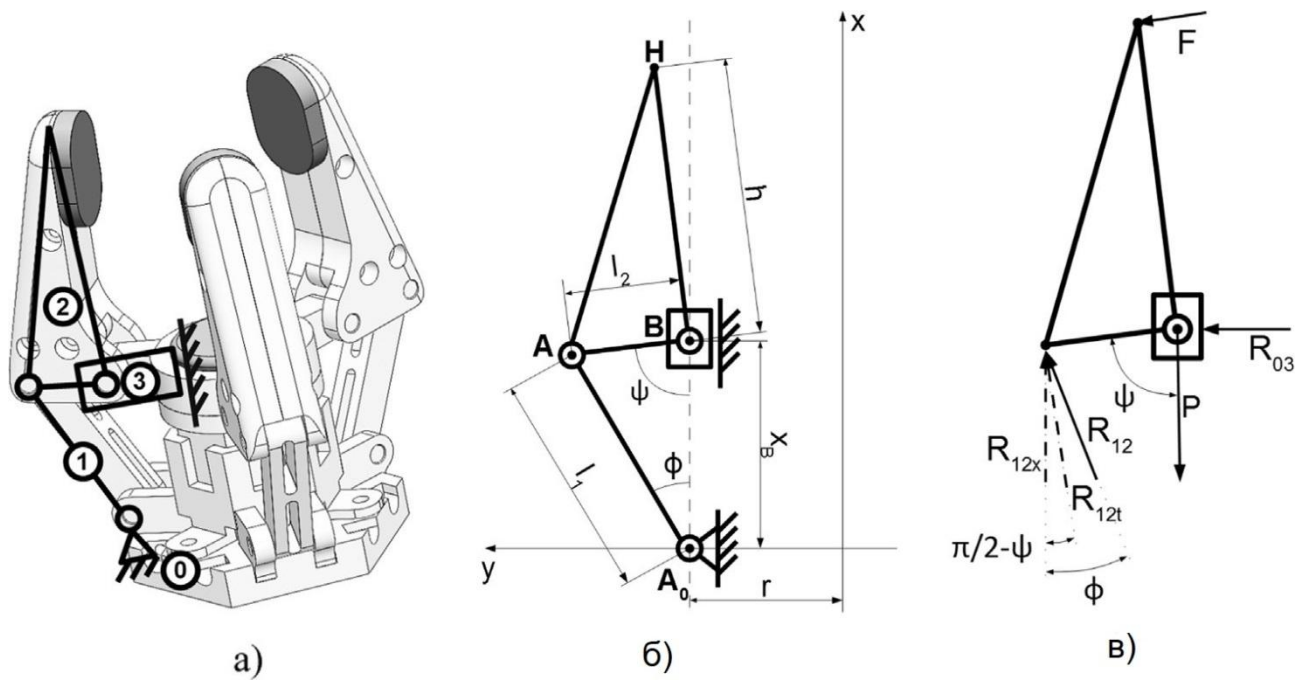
Трехфаланговый схват робота для захвата агро-садоводческой продукции: а) общий вид схвата; б) кинематическая схема схвата; в) кинетостатическая схема схвата
